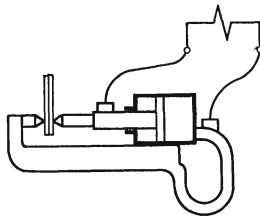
Schweißpistole mit Preßluftbetrieb.
